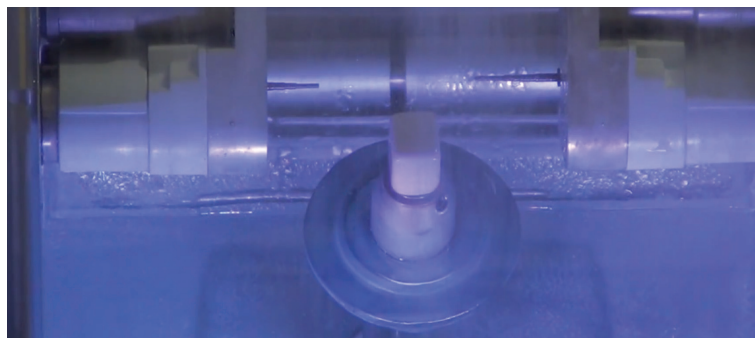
Usinage de la couronne (Dr Rick Miller)
